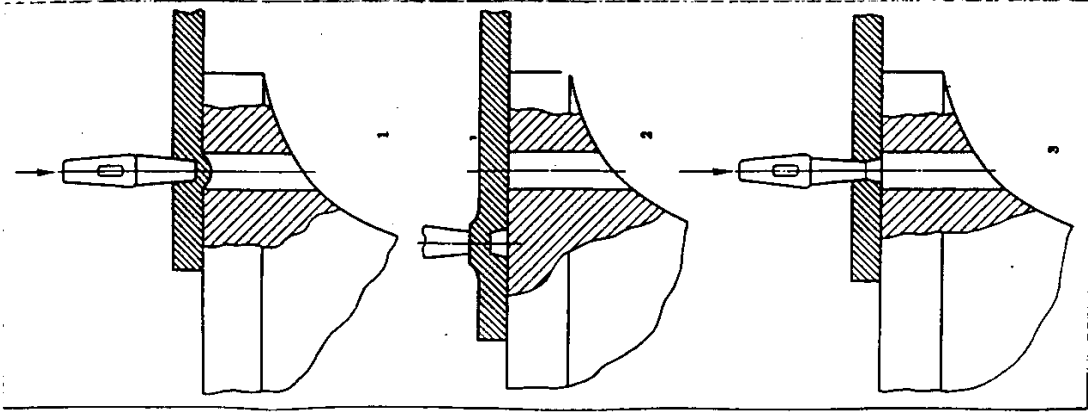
Пробивка отверстий: 1 — предварительная пробивка; 2 — параворот заготовки; 3 — окончательная пробивка
